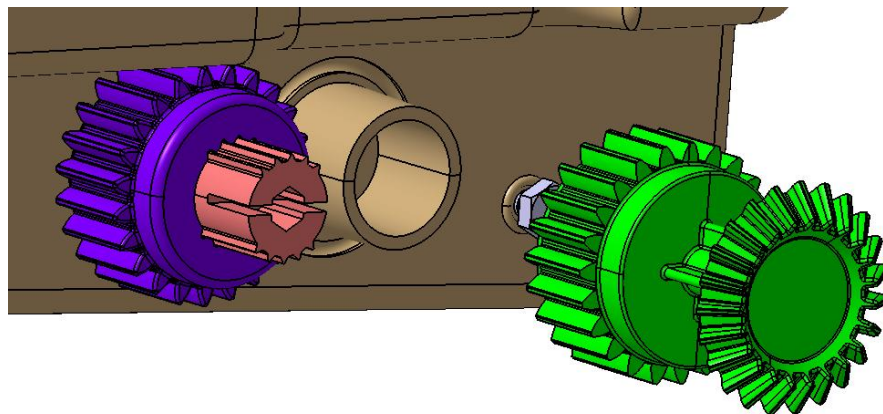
Montaje engranaje recto. [Elaboración propia]
